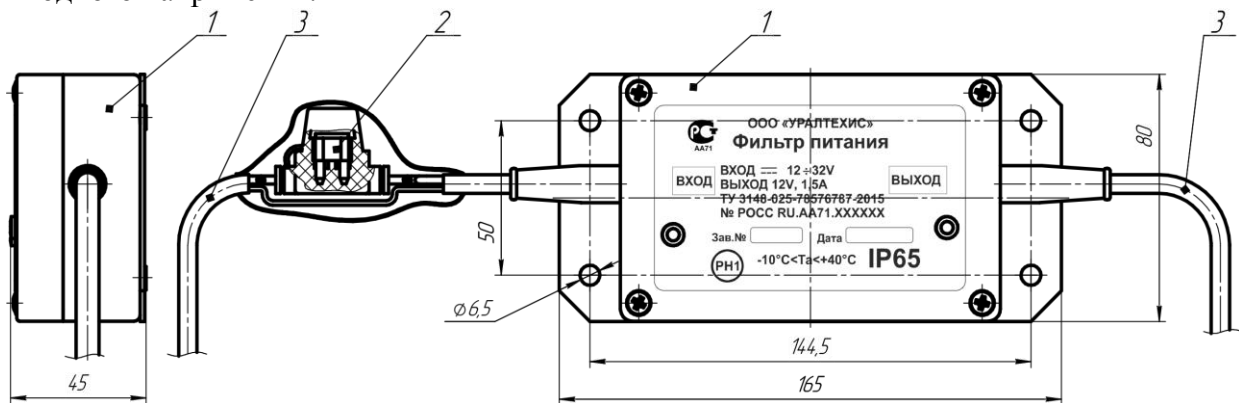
Внешний вид фильтр питания ФПН ТИС 2.1.9.02.000
